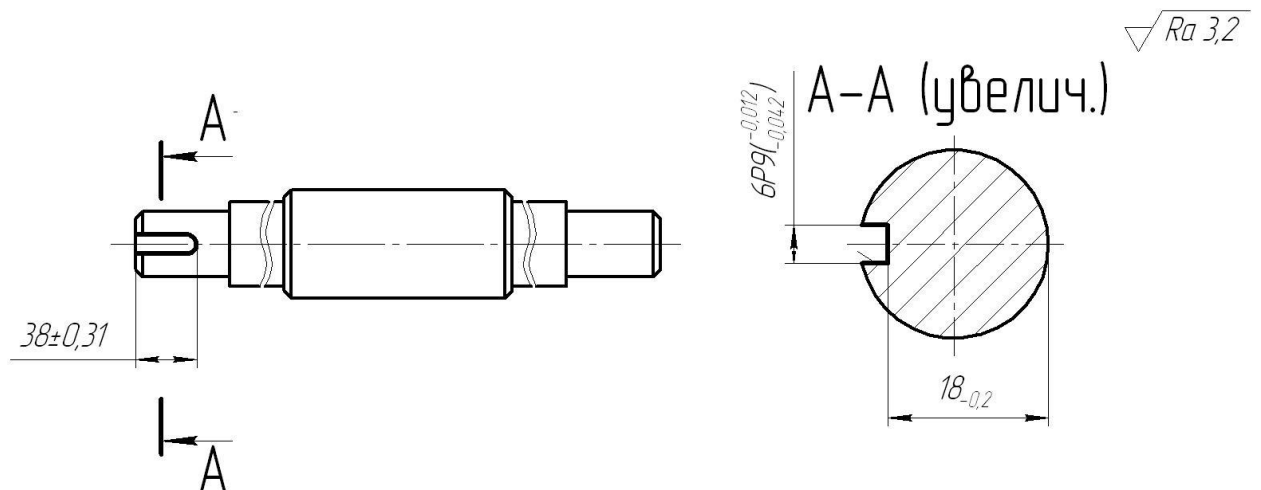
Эскиз шпоночно-фрезерной операции
